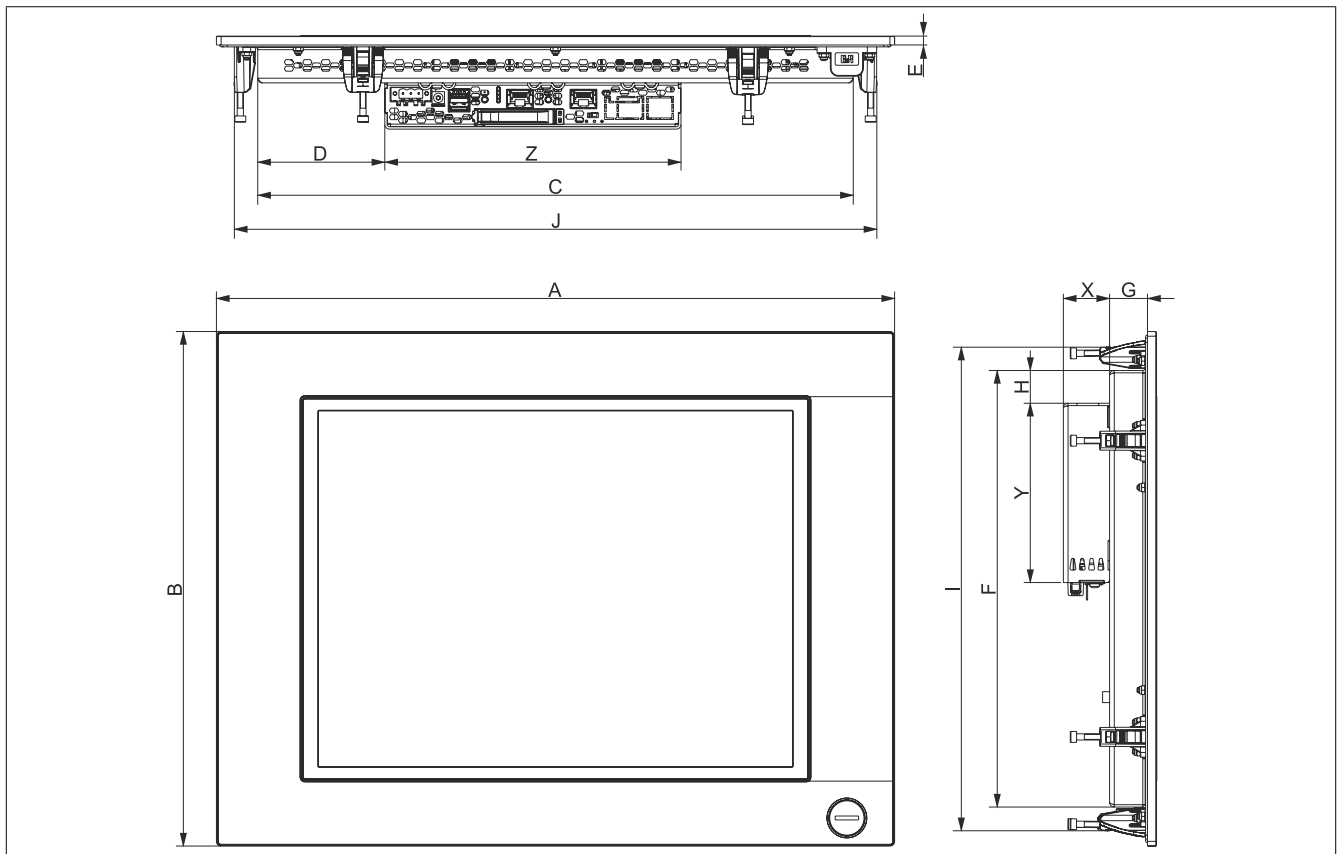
Abmessungen - Panel PC 2100 mit AP1000 Panels mit Klemmblocken (Beispielabbildung)
